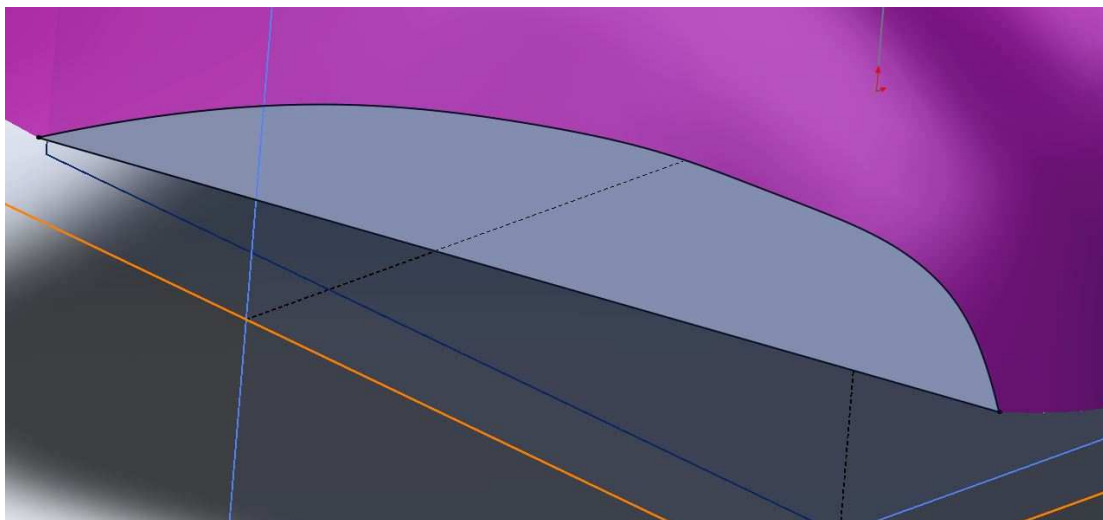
Ρυθμίσεις Surface fill μπροστινής πλευράς
